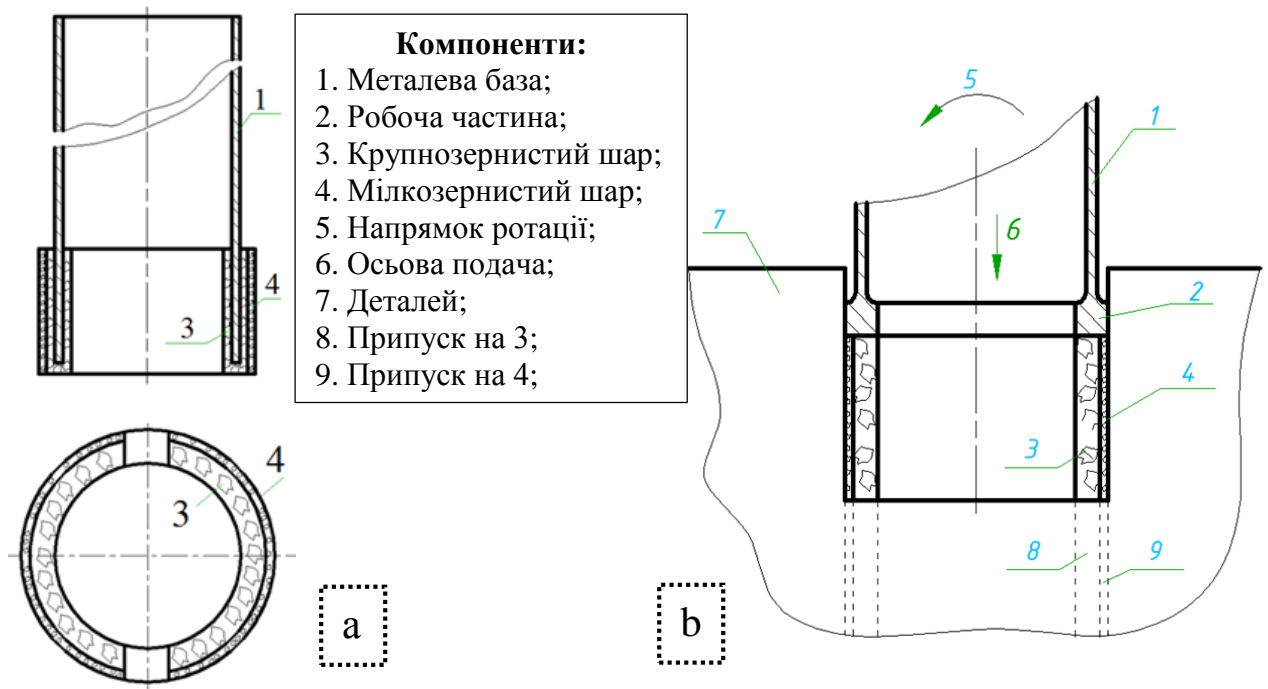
Авторська конструкція свердла (а) і схема видалення припуску різнозернистим інструментом (б) [121]
